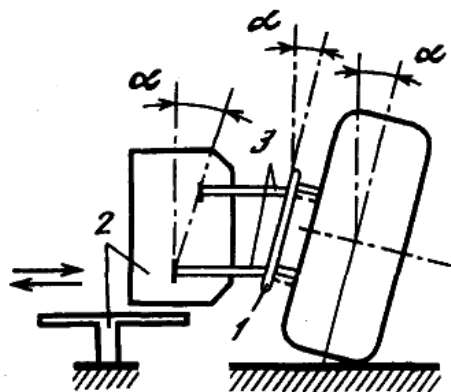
Контактный способ измерения углов установки колес: 1 – диск, устанавливаемый на колесо; 2 – измерительная головка с направляющими; 3 – контактные измерительные стержни
